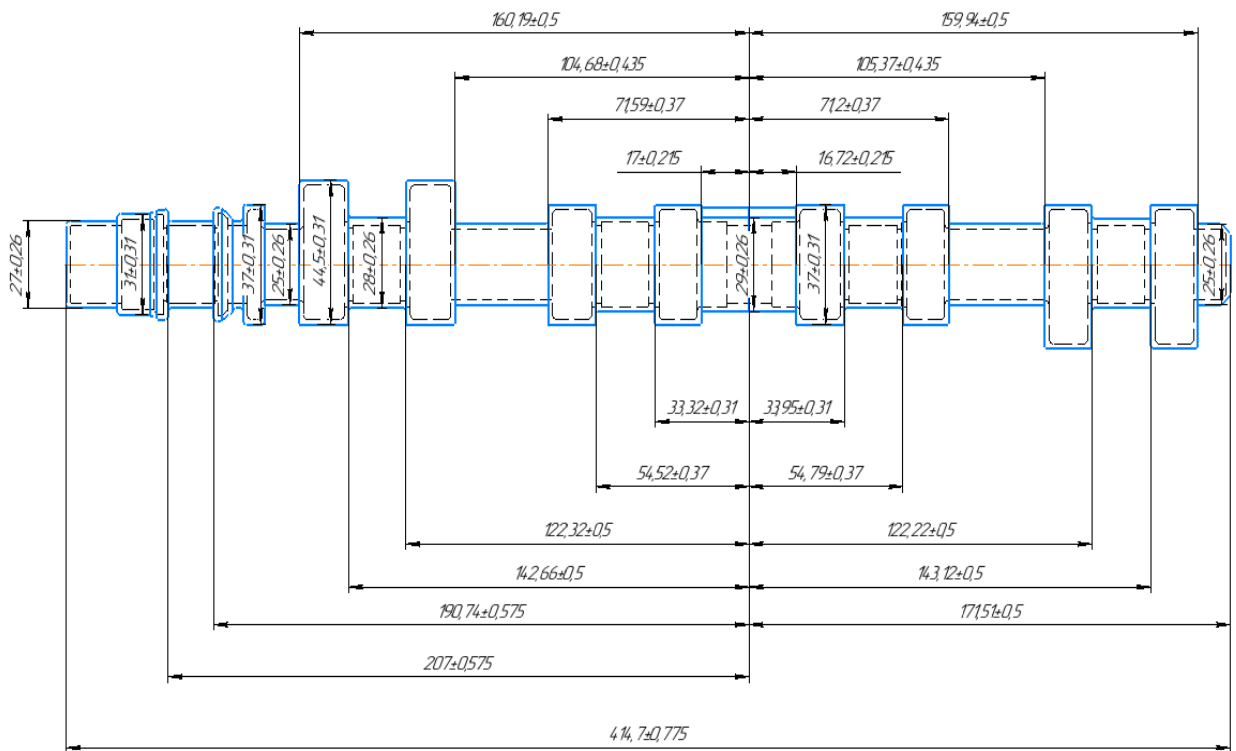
Чертеж заготовки распределительного вала в двигателе «ВАЗ - 21126».
